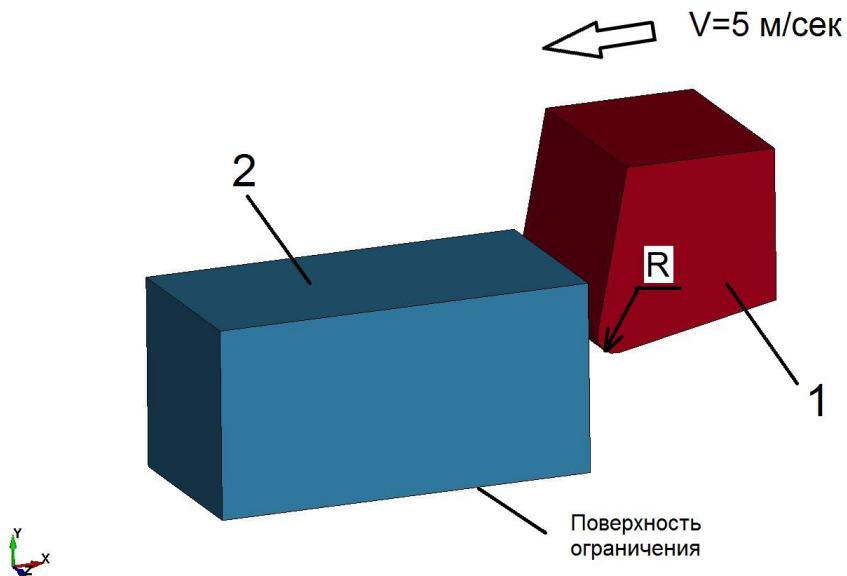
Схема процесса резания клином заготовки Лагранжевого типа: 1 – режущий клин с радиусом закругления при вершине R, 2 – заготовка
